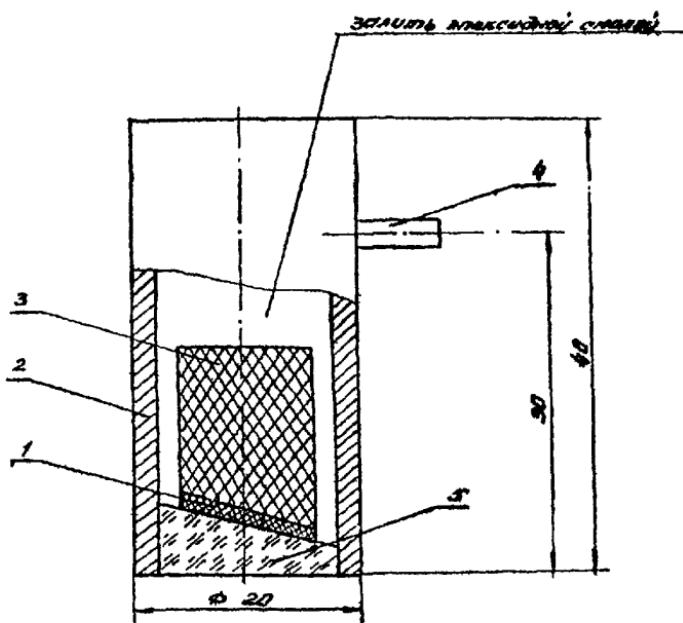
Рис. I. Наклонный совмещенный с углом призмы $10^0(13^0)$: 1 - пьезопластина ; 2 - корпус ; 3 - демпфер ; 4 - разъем ; 5 - призма.
